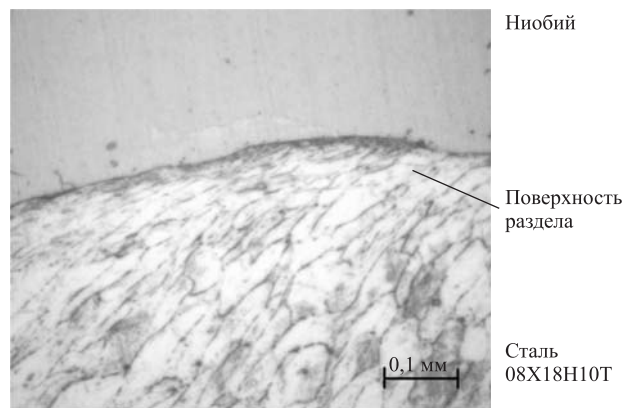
Микроструктура сварного соединения ниобия и стали 08X18H10T, выполненного методом сварки взрывом
